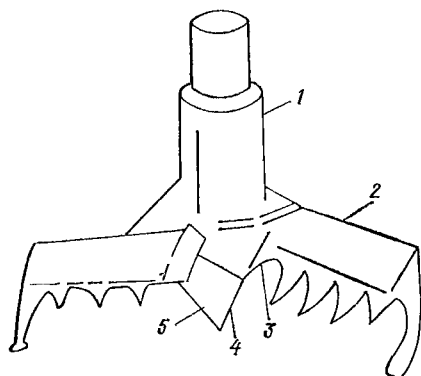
Общий вид трехперового бура конструкции ВНИРО [147].
